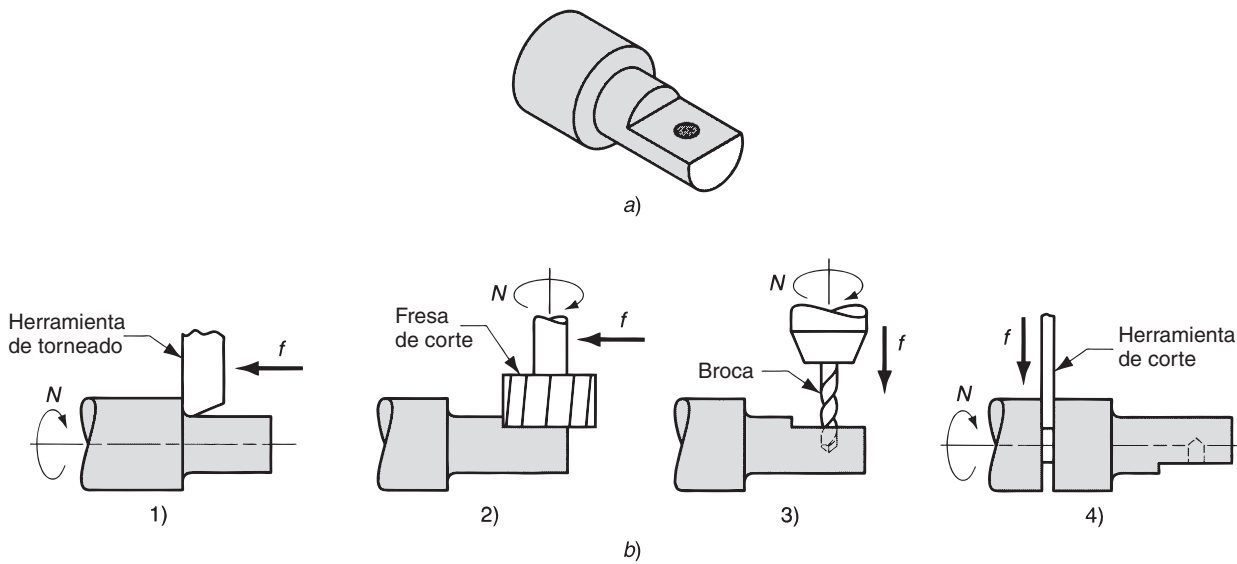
Operación de un centro de torneado y fresado: a) ejemplo de una pieza con superficies torneadas, fresadas y taladradas y b) secuencia de operaciones en un centro de torneado y fresado: 1) torneado de un segundo diámetro, 2) fresado plano en una posición angular programada de la pieza, 3) taladrado de un agujero con la pieza en la misma posición programada y 4) corte.
